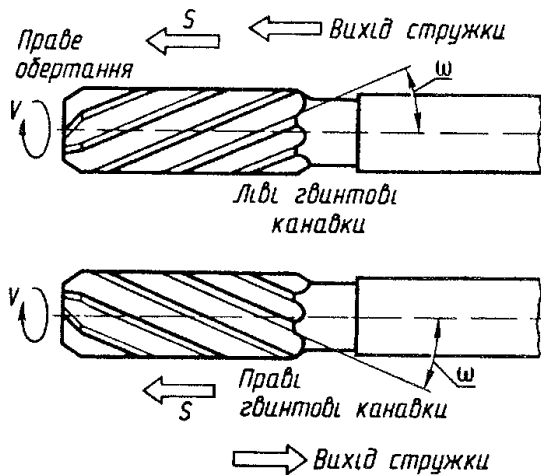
Розвертка зі спіральними (гвинтовими) канавками:
